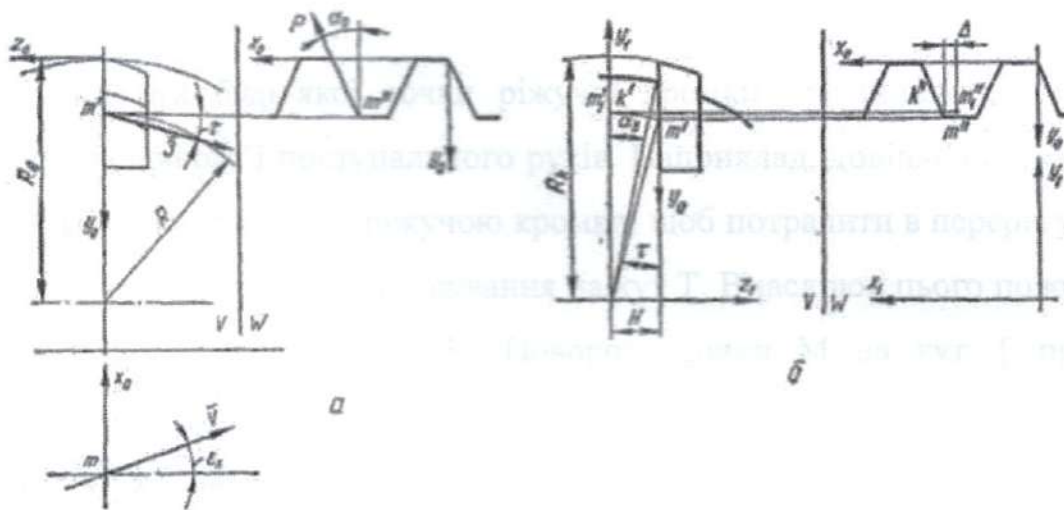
Схема затилування черв'ячних фрез «по колу»
